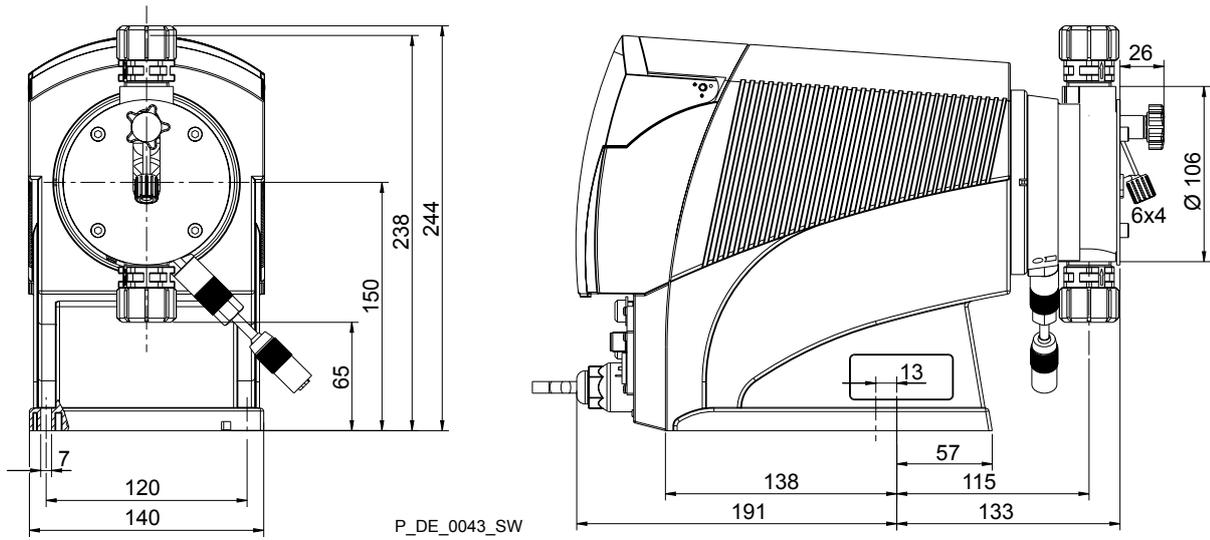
Maßblatt delta® Typ 0450 - 0280, Werkstoffausführung PV - Maße in mm
